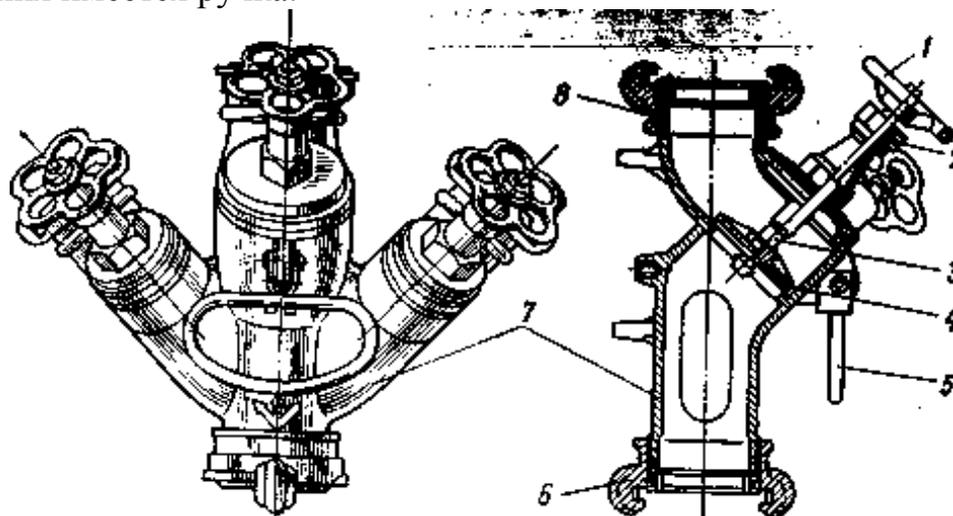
Разветвление трехходовое РТ: 1 – маховичок; 2 – уплотнитель сальниковый; 3 – шпиндель; 4 – тарельчатый клапан; 5 – ручка; 6 – входной патрубок; 7 – корпус; 8 – выходной патрубок
